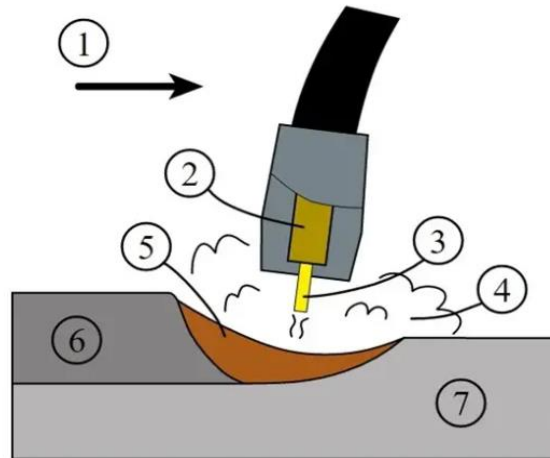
Principe du procédé de soudage MIG (131)/MAG (135) [6]
